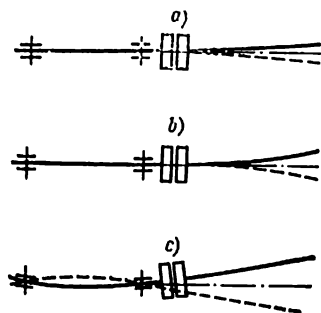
Battement de l'arbre d'un rotor à un seul support dû : a) au battement des faces frontales des plateaux ; b) au gauchissement de l'arbre d'un rotor à un seul support ; c) au gauchissement de l'arbre d'un rotor à deux supports
